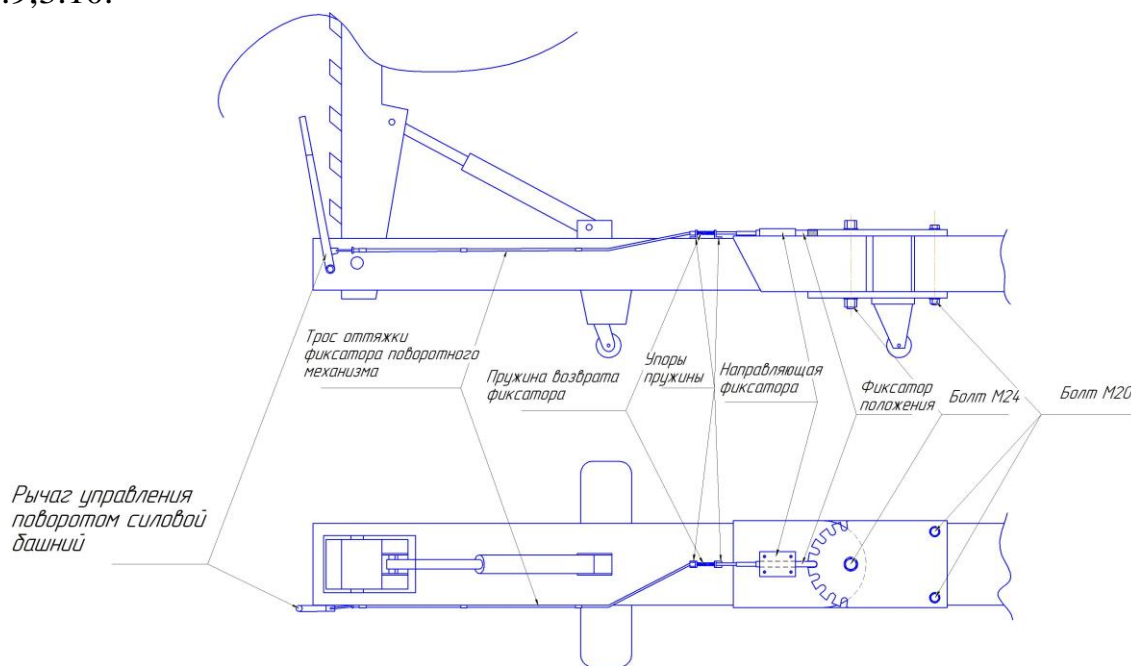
Принципиальная схема устройства поворотного механизма силовой башни стапеля с ручным управлением
